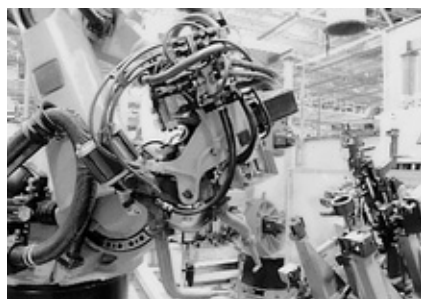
Гибкий производственный роботизированный модуль для сварки кузовов легковых автомобилей
